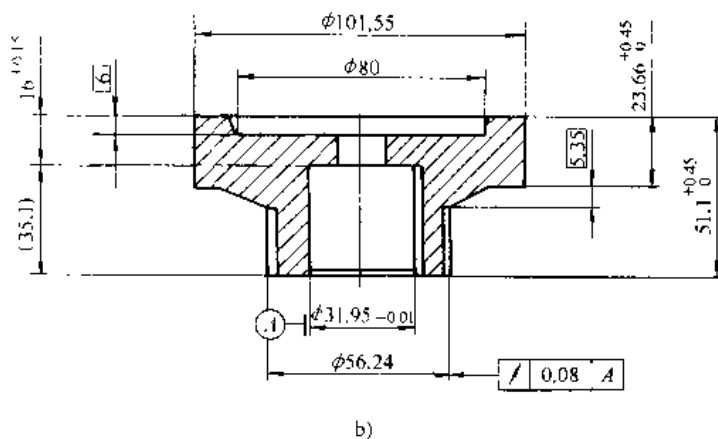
汽车发动机轮毂压坯成形模具 (续)
